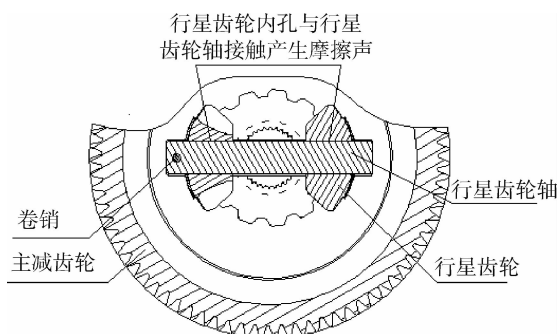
行星齿轮与行星齿轮轴摩擦产生噪音的部位
